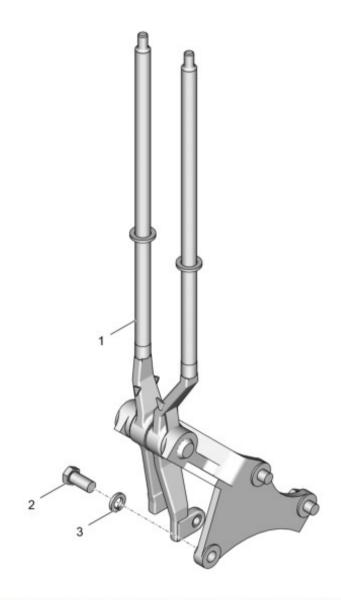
4320Я2-1804003 Установка рычагов управления раздаточной коробки
